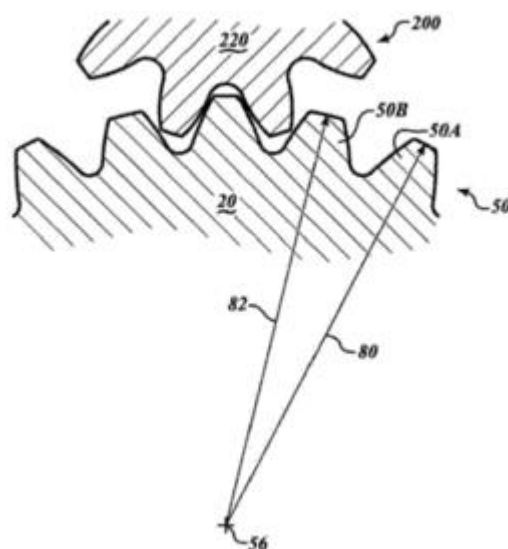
Зубчатое колесо, образованное червячной фрезой
